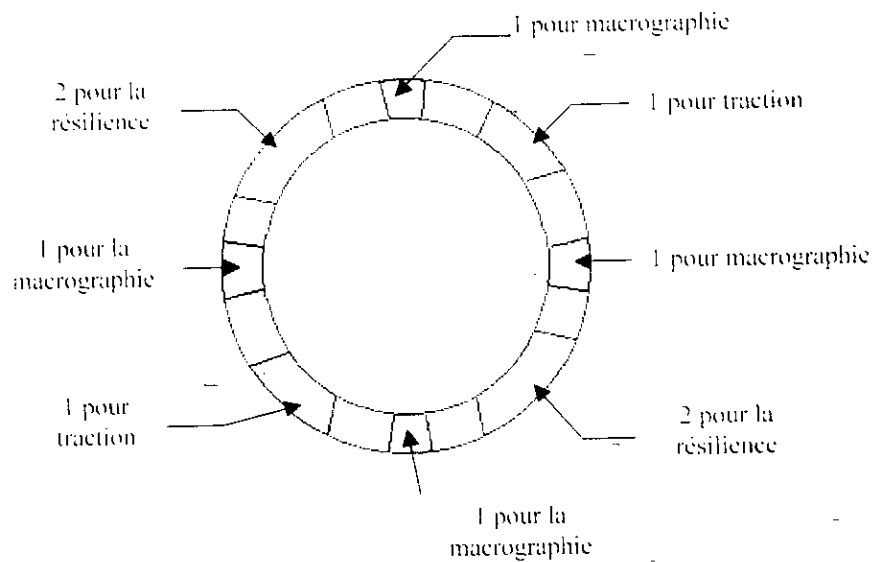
Schéma de prélèvement des éprouvettes pour la caractérisation des joints soudés.
